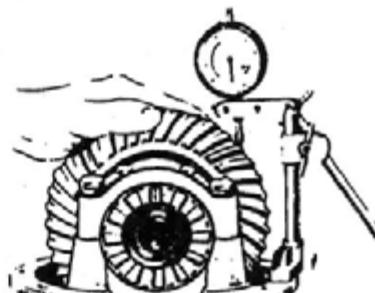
Проверка бокового зазора в зацеплении зубьев ведущей и ведомой шестерен главной передачи при помощи индикатора
